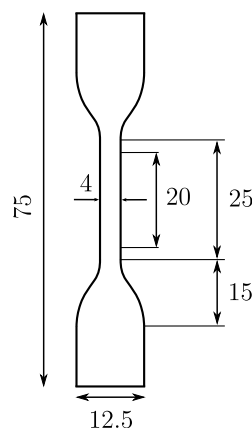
Géométrie des éprouvettes H2. Les dimensions sont en mm.
